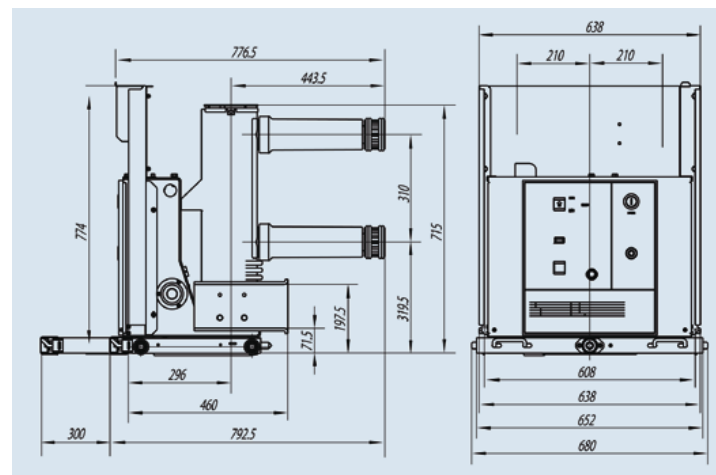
Внешний вид и размеры выключателя серии NV1-24
